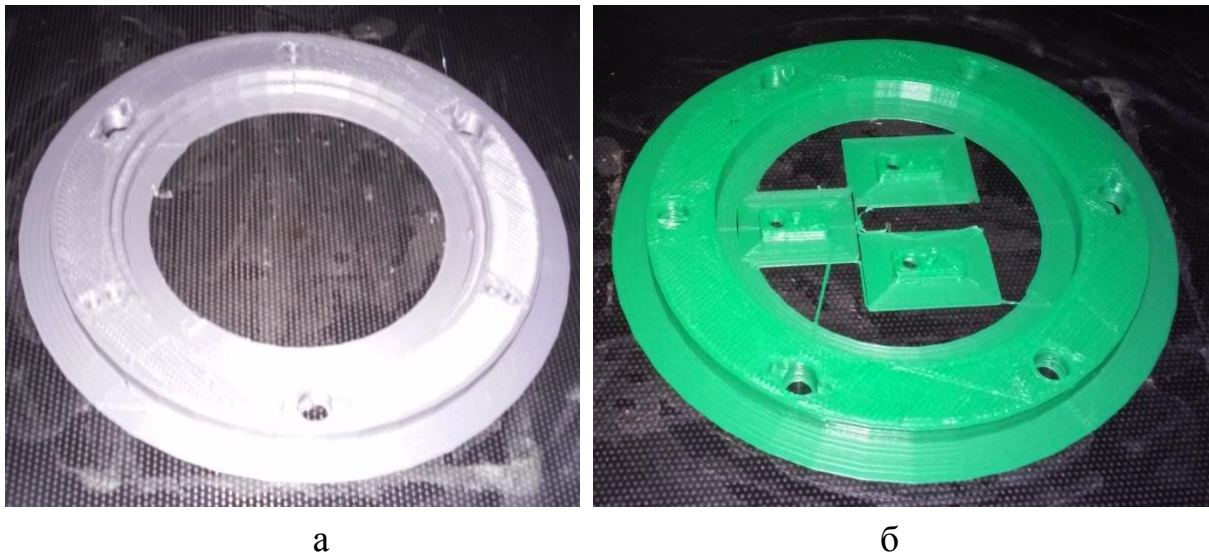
Роздруковані на 3D-принтері деталі: а) оправа; б) основа з планками
